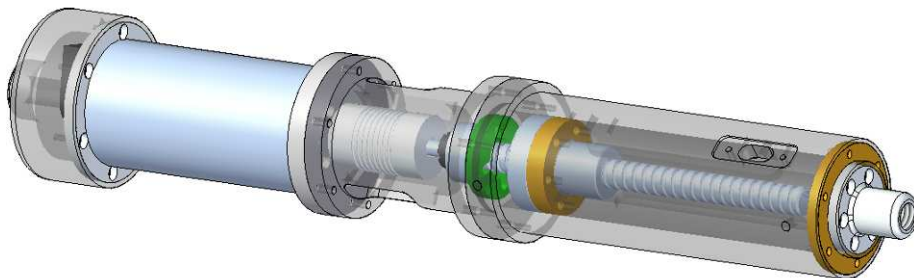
Montaje del conjunto del husillo en el motor
